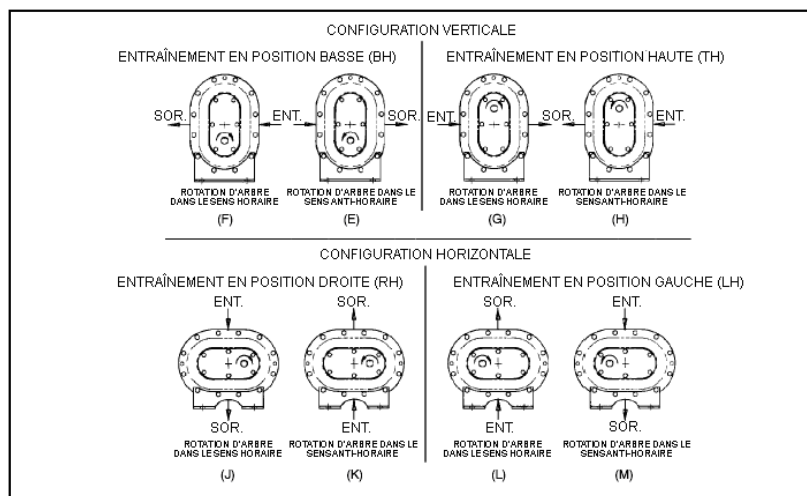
CONFIGURATIONS DE MONTAGE DU VENTILATEUR
